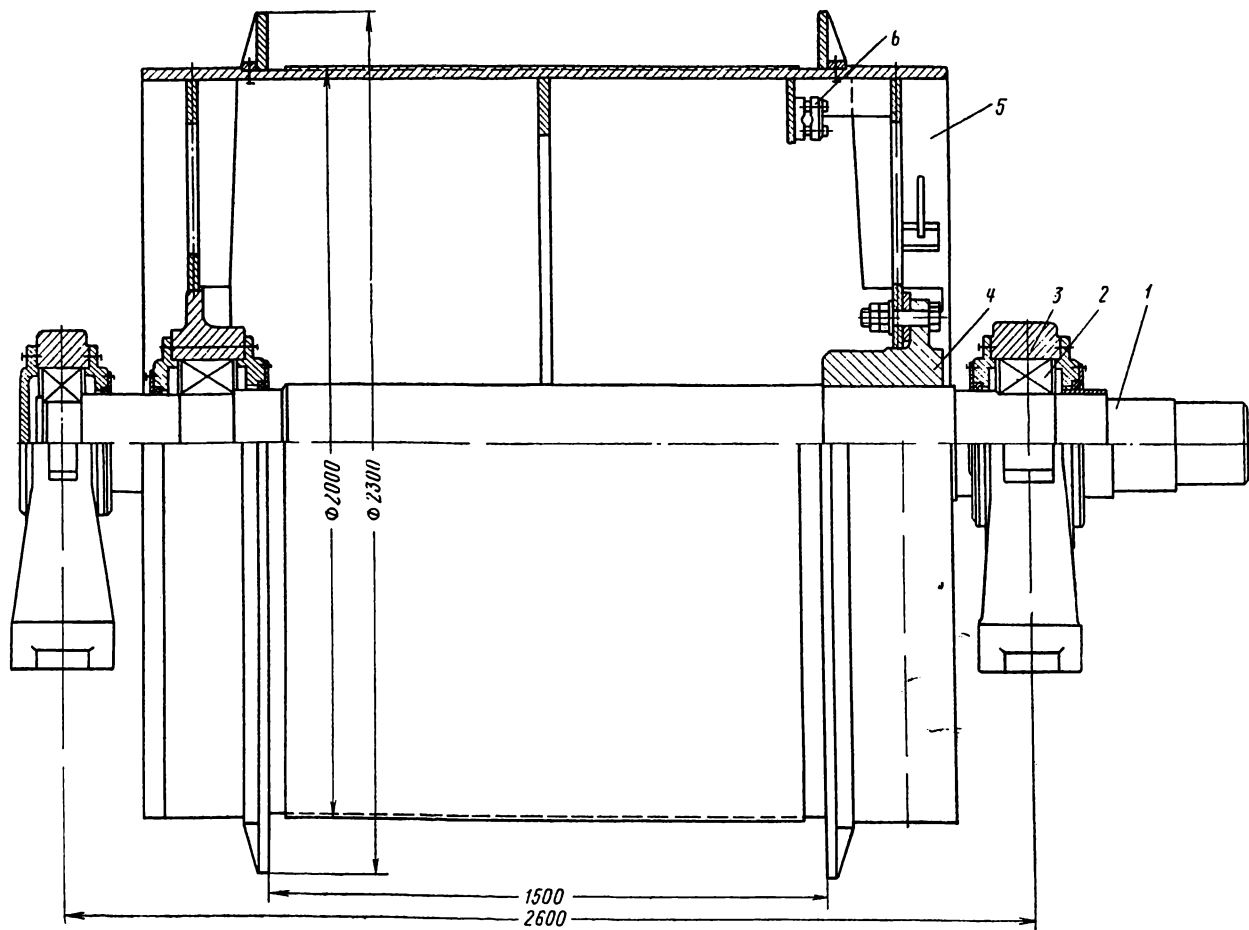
Сборка главного вала машины Ц-2×1,5:
